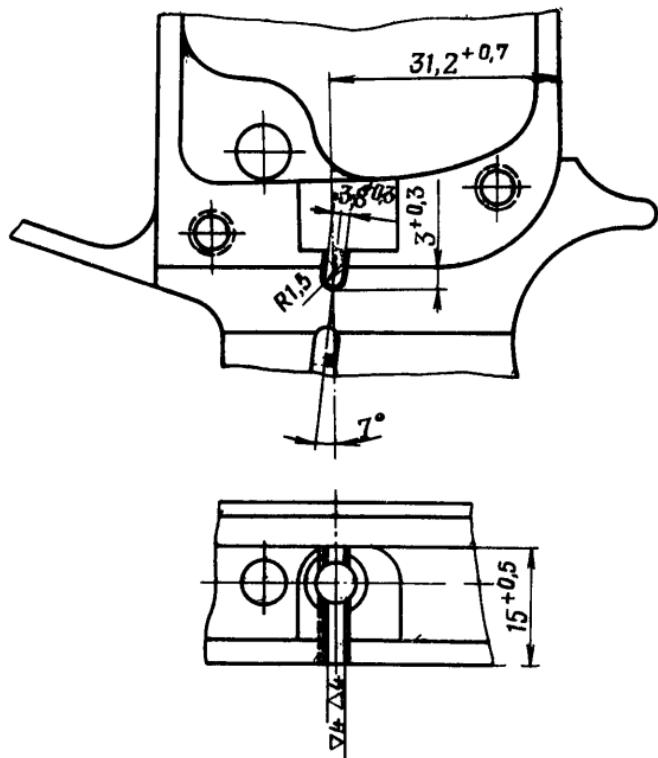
Фрезерование паза под выколотку в корпусе ударно-спускового механизма
